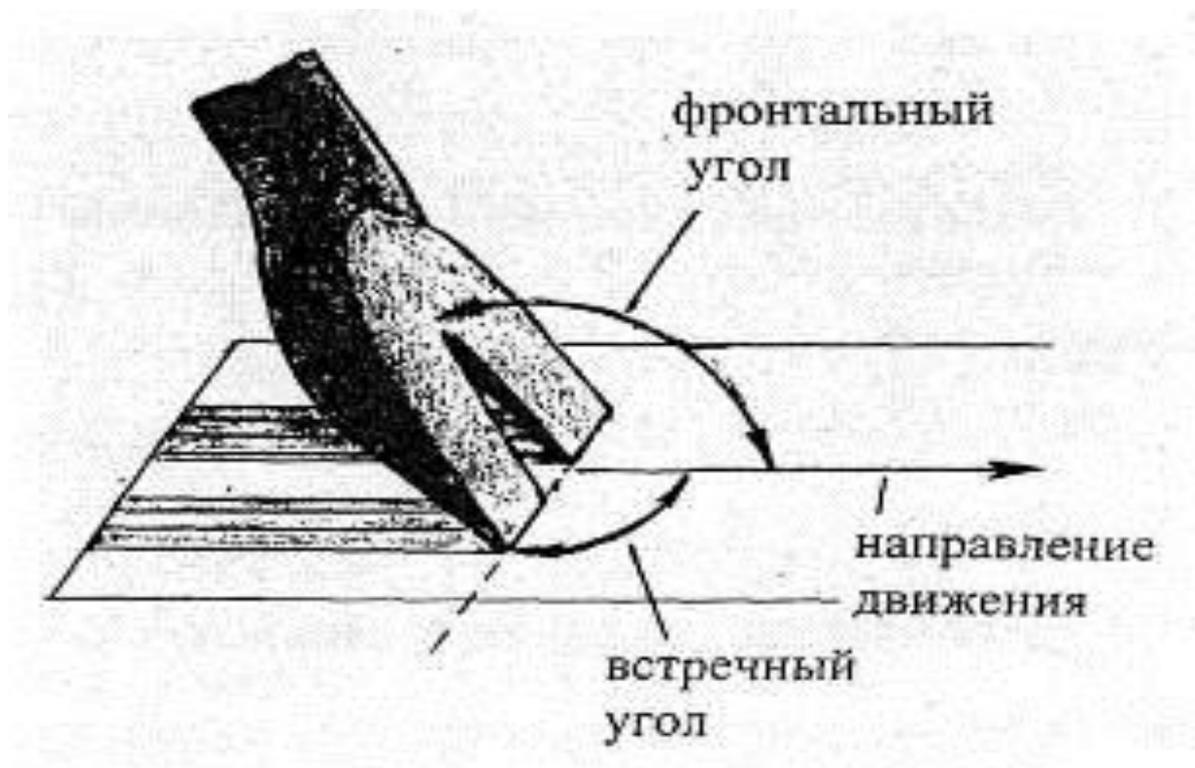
Фронтальный и встречный углы, приложения инструмента.
